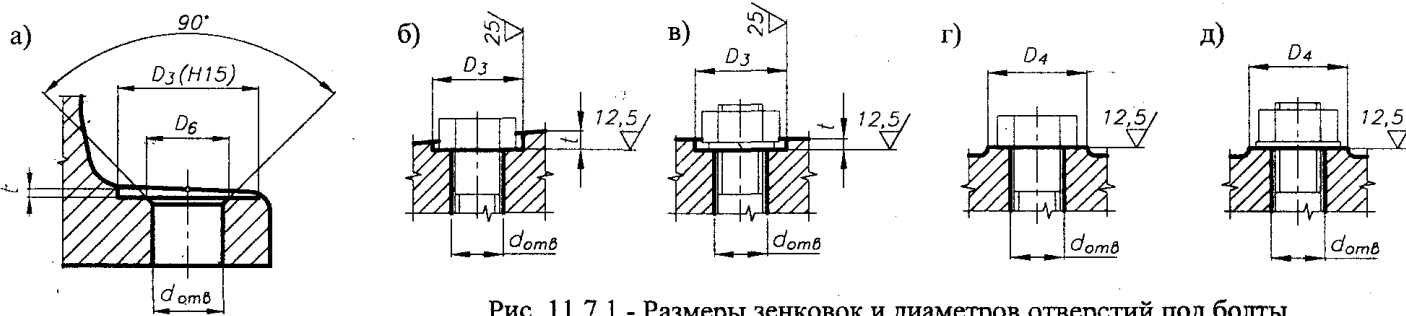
Размеры зенковок и диаметров отверстий под болты
